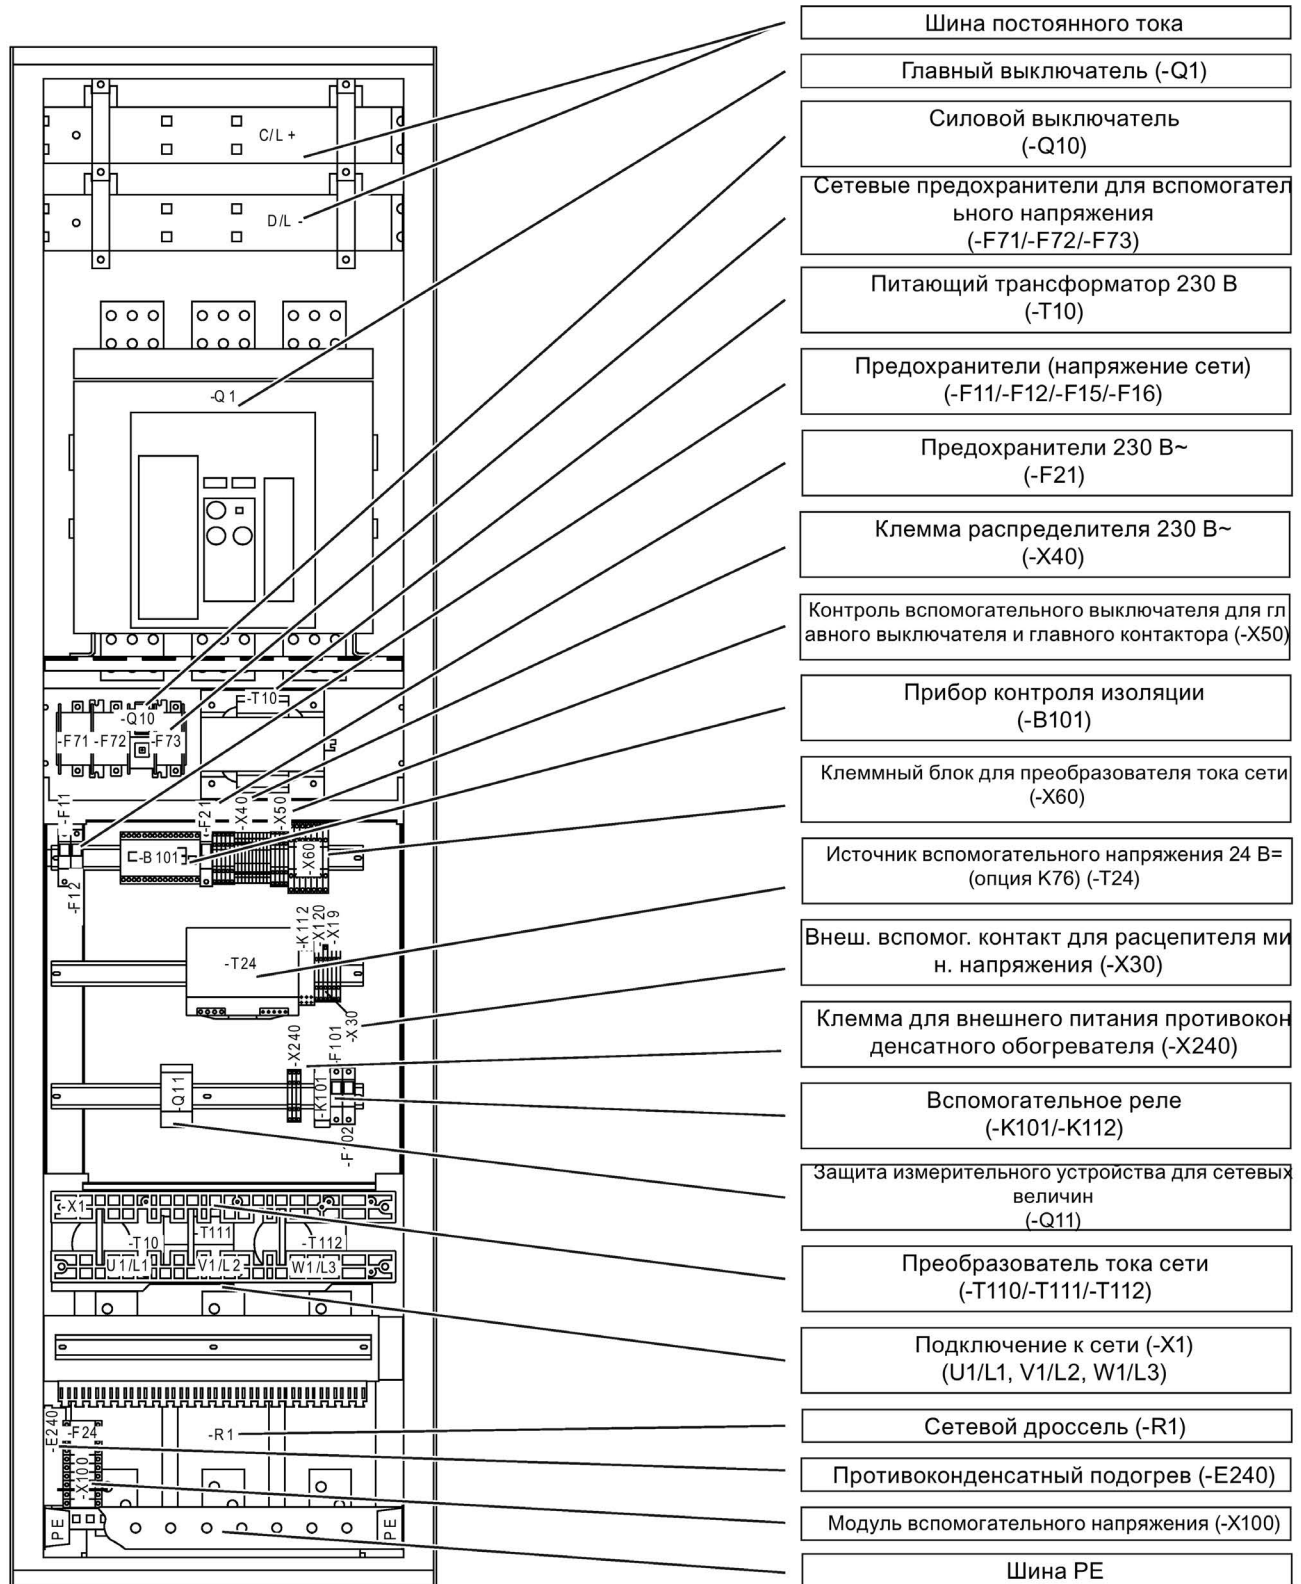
Пример сборки соединительного модуля питания (типоразмер JL)
